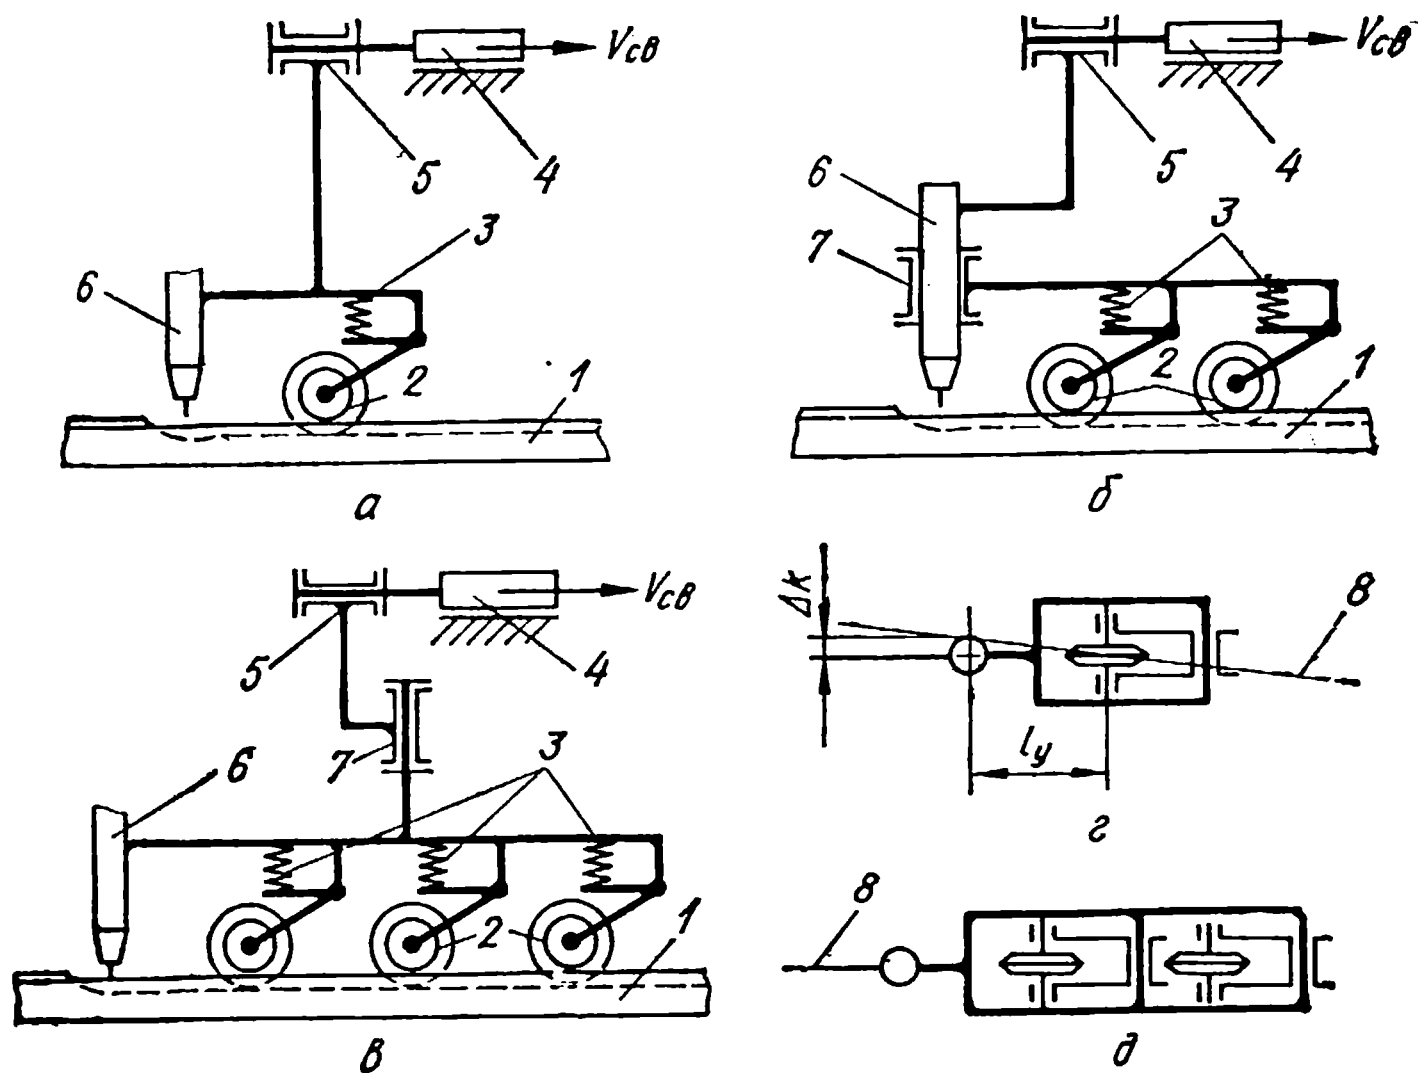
Схемы устройств прямого действия для направления сварочного инструмента по линии соединения:
